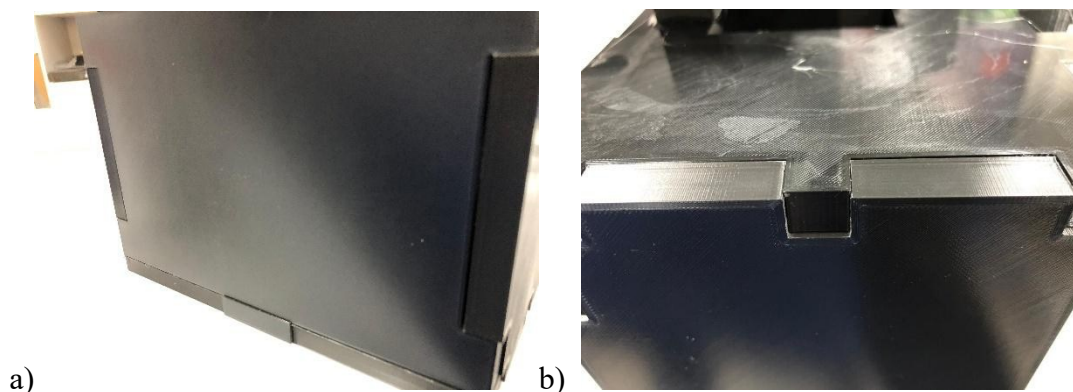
Estrutura fixa com destaque para os encaixes de pressão.
